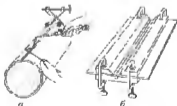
Зажимные приспособления для сварки с переменным (а) и постоянным (б) зазором
